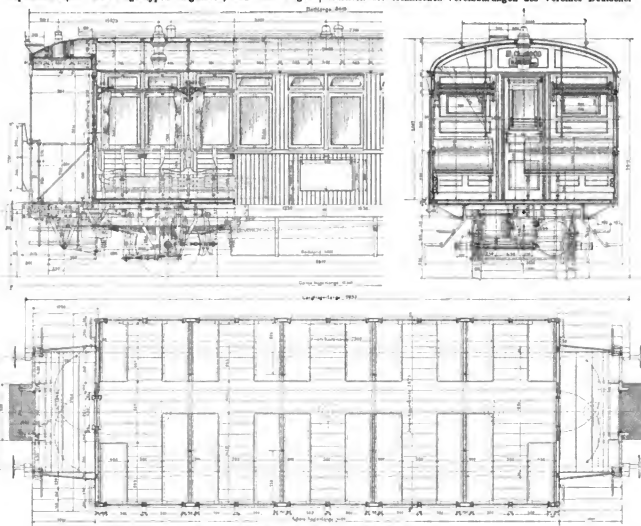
, 6 und 7. Längenschnitt, Querschnitt und Grundriss der Wagen III. Cl.
